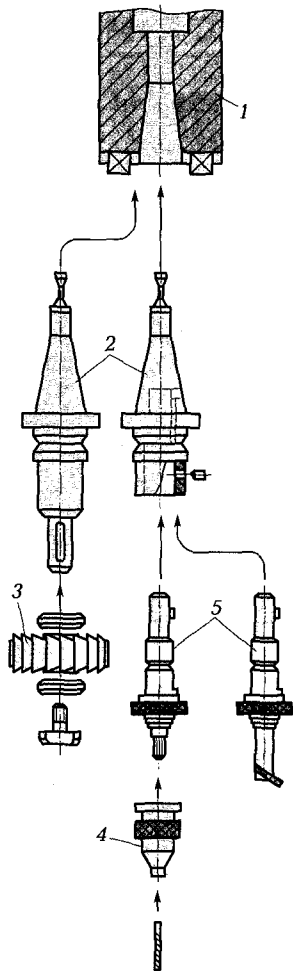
Схема построения инструментального комплекта для многоцелевых станков:
